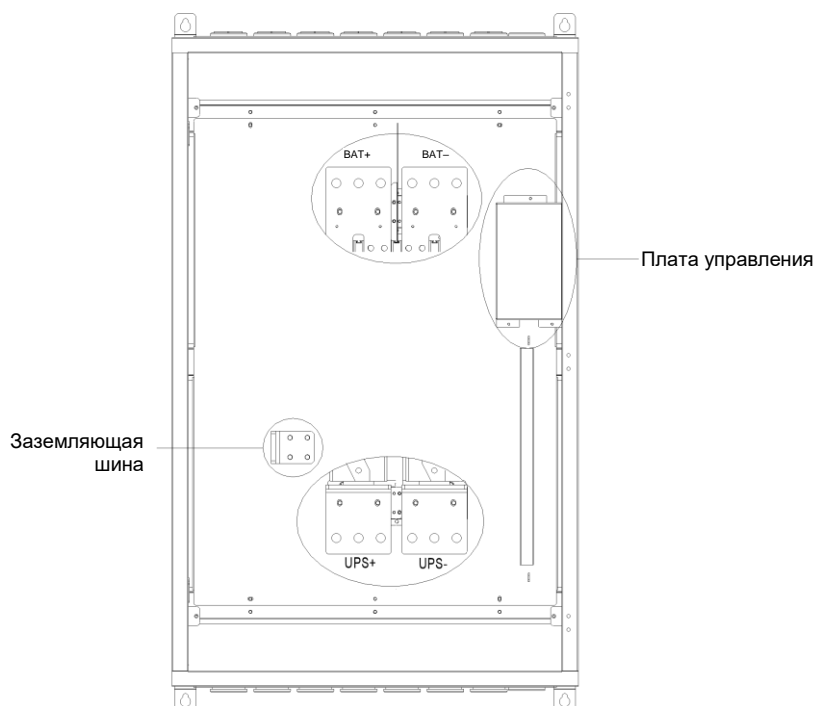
Внутренняя конструкция батарейного автомата ИБП 800 кВА (размеры в мм)
